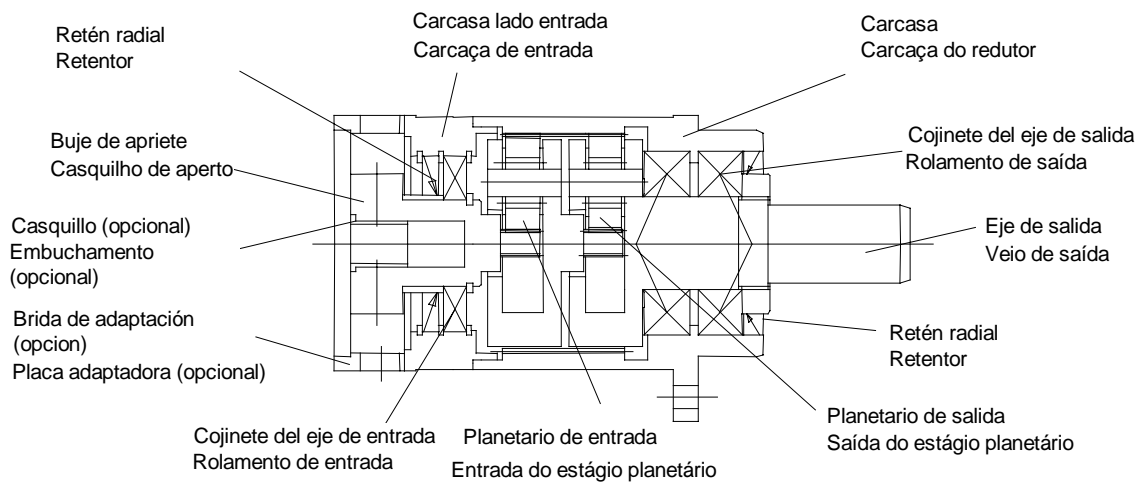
Diseño técnico de la versión de dos etapas y montaje sobre motor
